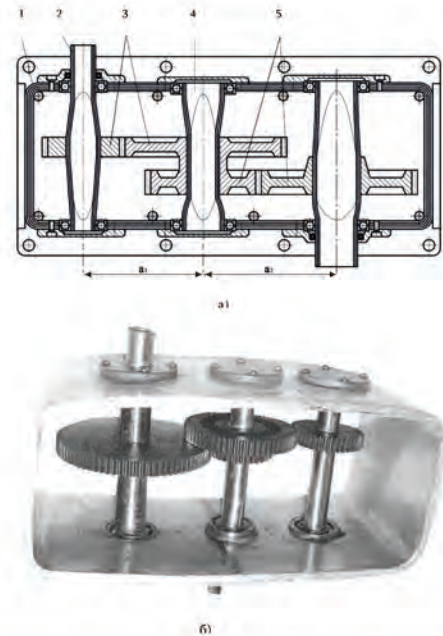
Адаптивный редуктор: а) продольный разрез, б) общий вид, крышки сняты, 1 – корпус; 2, 4 – валы; 3, 5 – зубчатые передачи
